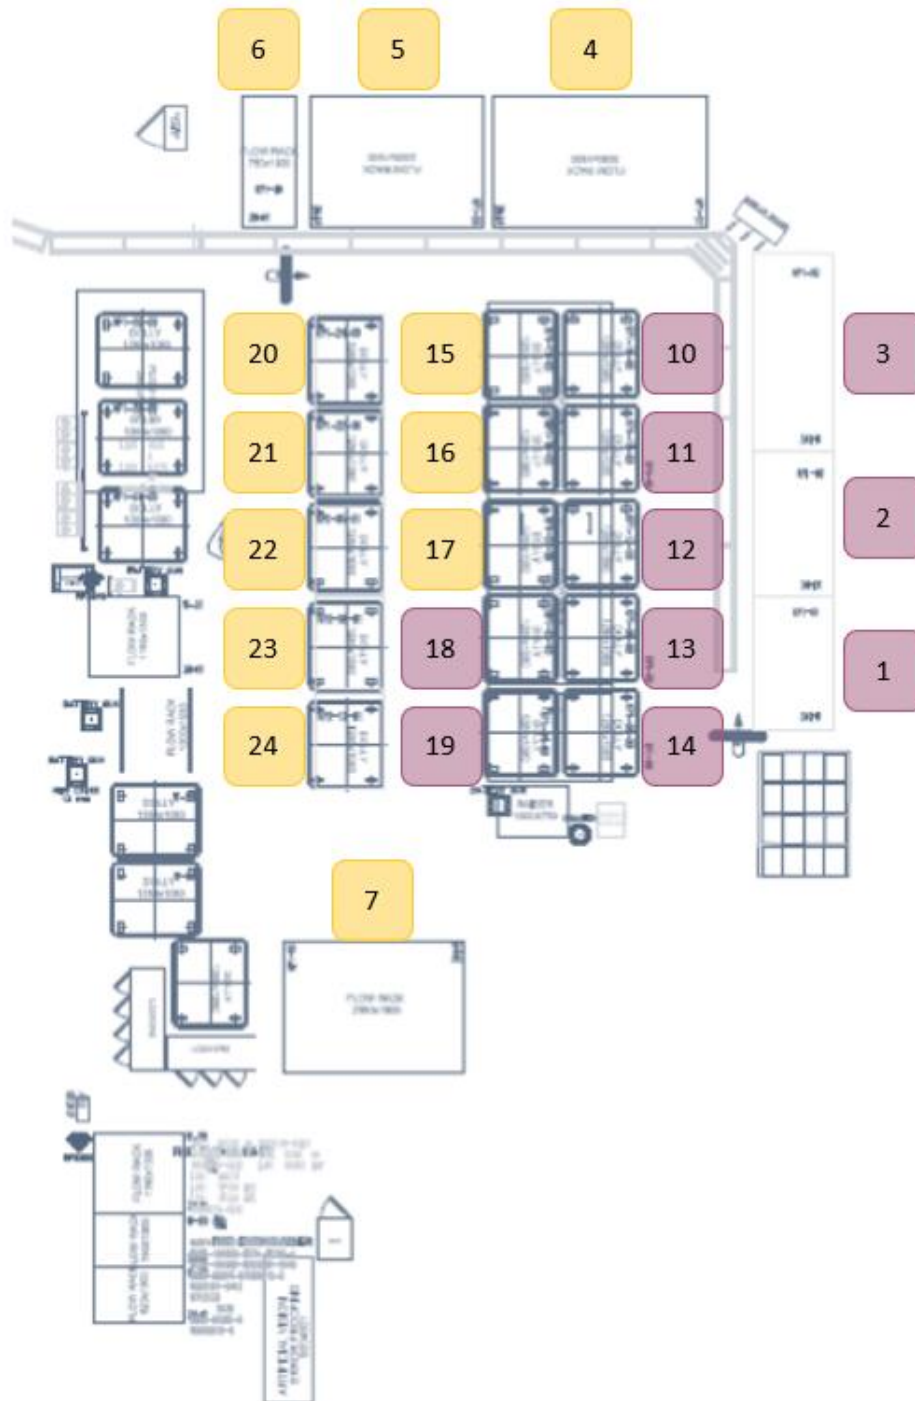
Propuesta 2 Layout KP1 Detallada (Fuente: elaboración propia)
